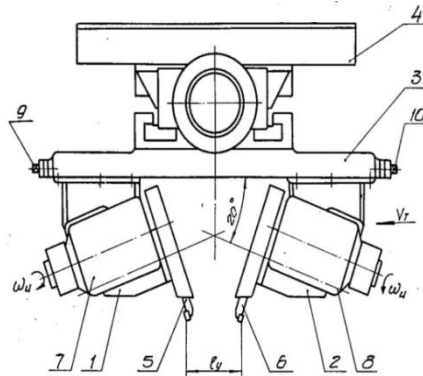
Принципиальная конструкция двухшпиндельного спецсуппорта к зубофрезерному станку мод. 5343
